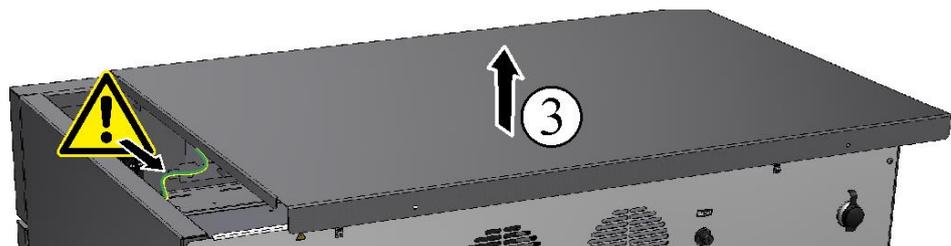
Soulever et déposer le couvercle (figure analogue)
